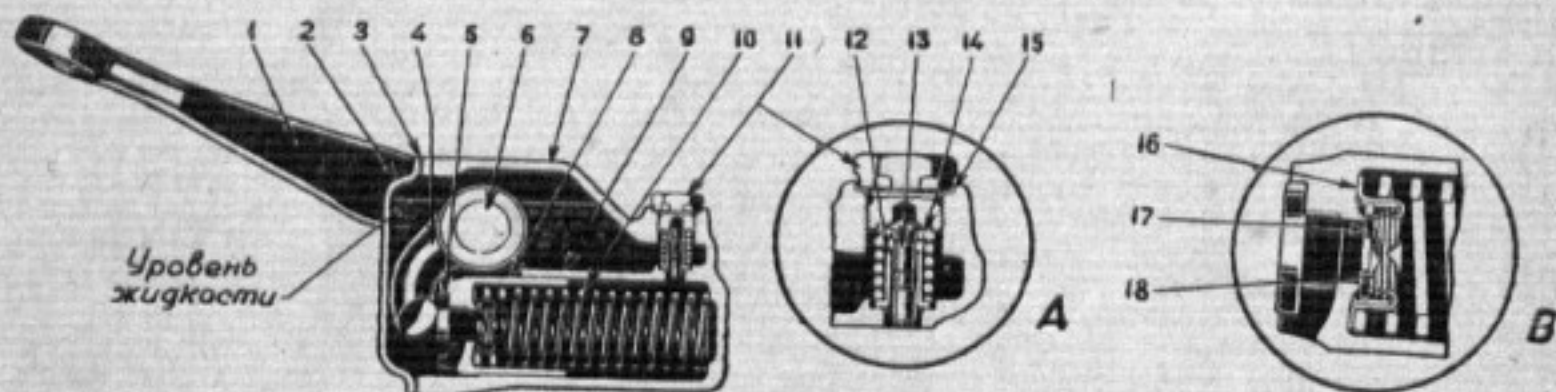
Продольный разрез амортизатора автомобиля М-1
